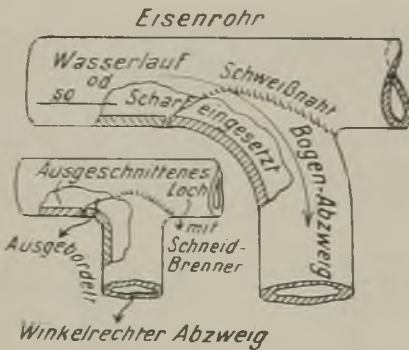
Anschweißen eines Bogenabzweiges.
